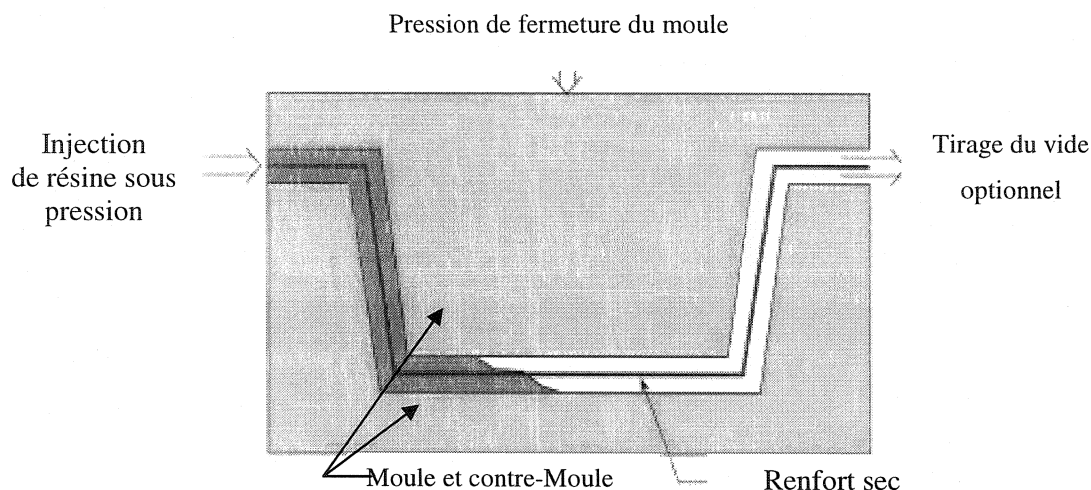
Procédé de moulage par RTM (réf. [5])
